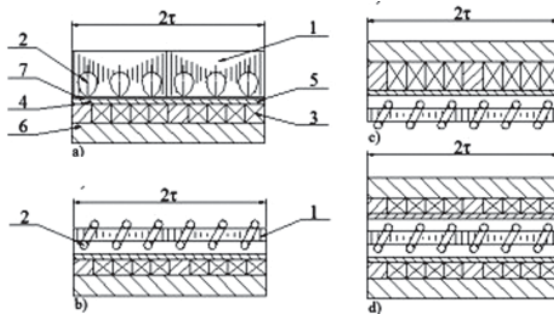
Конструктивные модели синхронного двигателя с постоянными магнитами (1 — сердечник статора; 2 — обмотка статора; 3 — магниты; 4 — немагнитные вставки; 5 — втулка; 6 — сердечник ротора; 7 — воздушный зазор)
